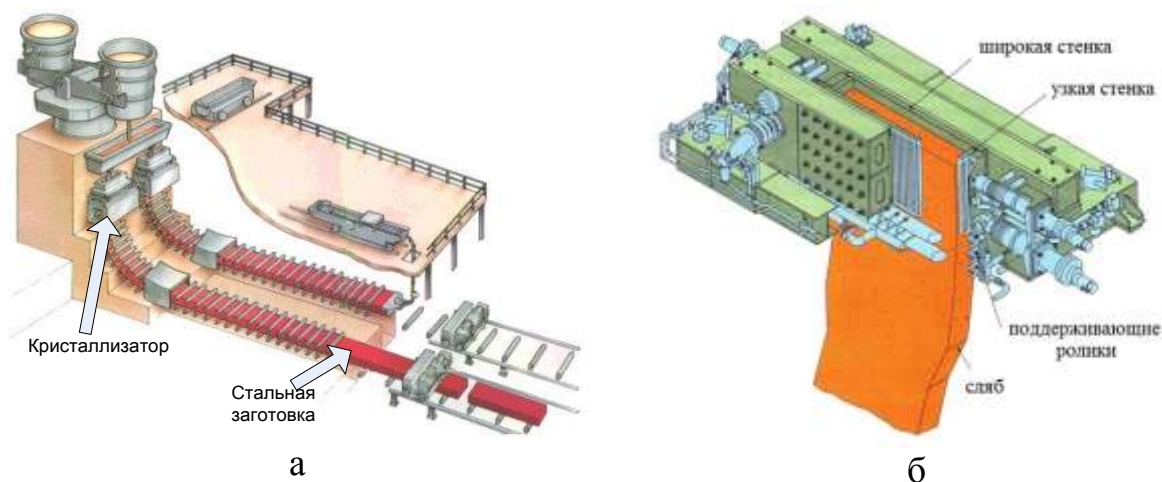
Схема процесса непрерывной разливки стали (а) и конструкция кристаллизатора слябового типа (б)
